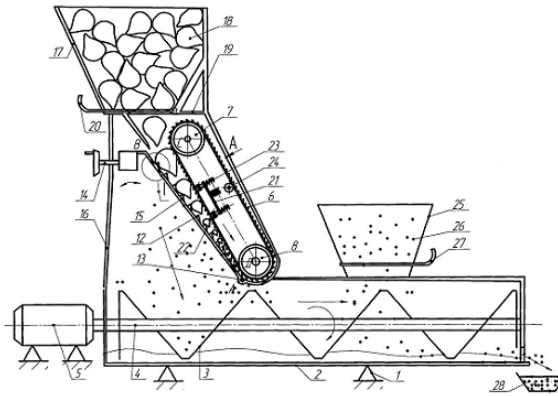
Конструктивна схема установки для подрібнення і змішування кормів
